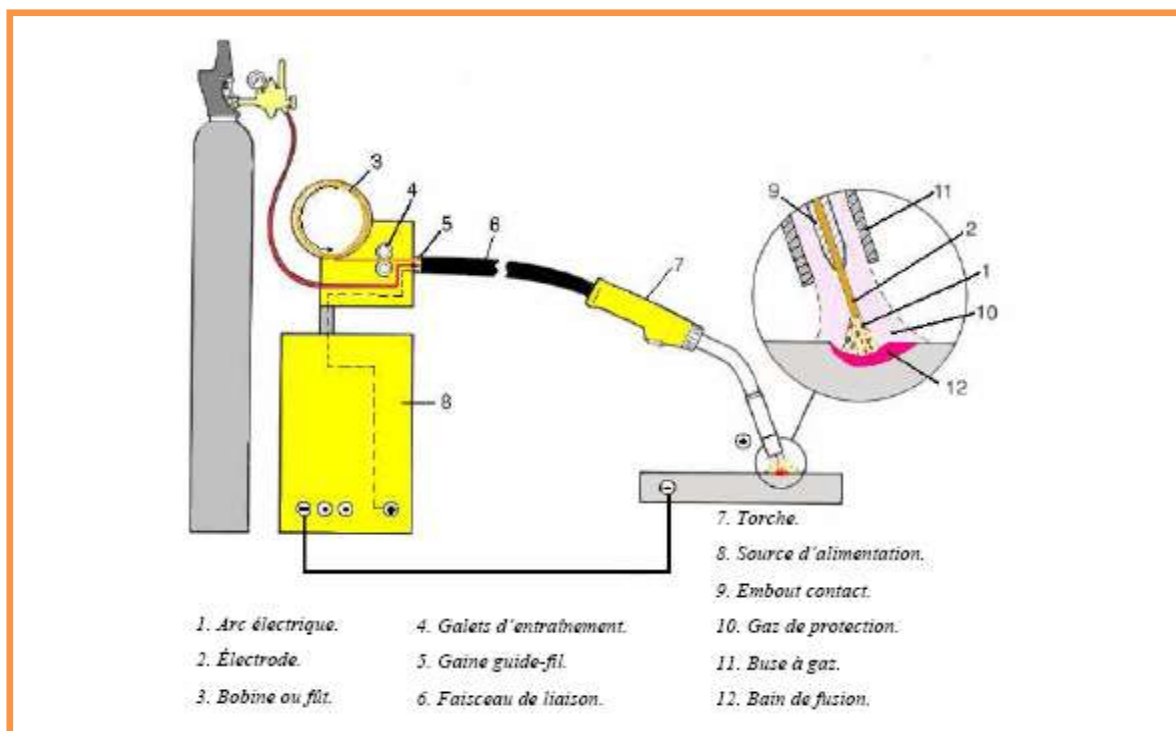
Principes du procédé de soudage MIG/MAG. [20]
